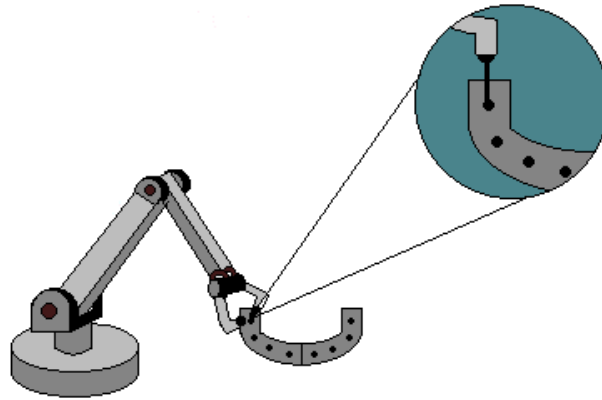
Ubicación del robot en un punto de soldadura.
